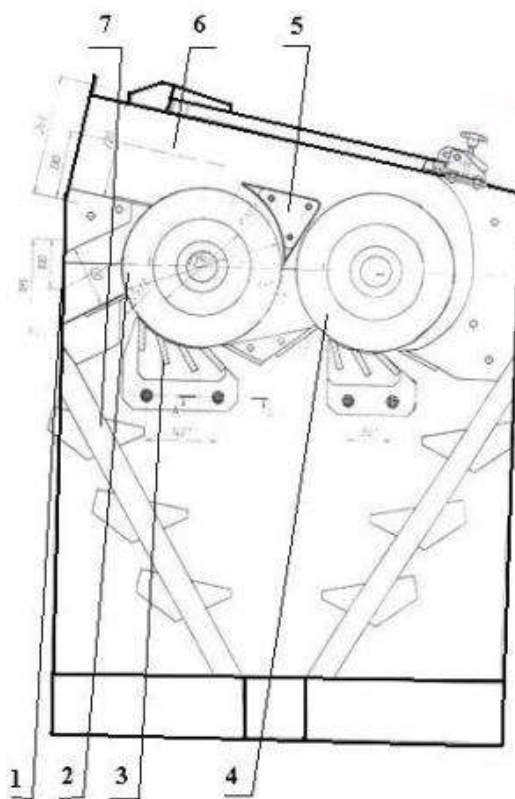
Двухбарабанный прямоточный волокноочиститель марки 2-ВПМ
